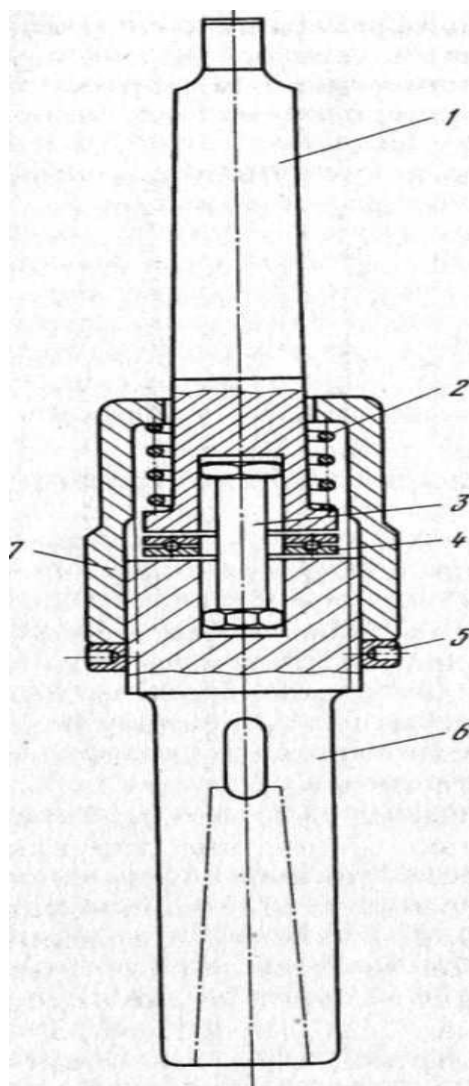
Самоустанавливающийся сверлильный патрон.
